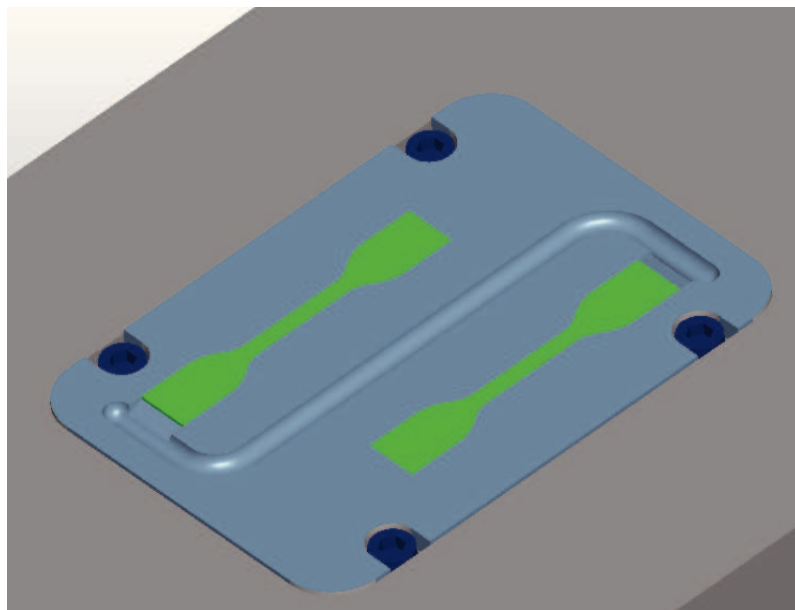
Fixação frontal do elemento moldante em material polimérico
